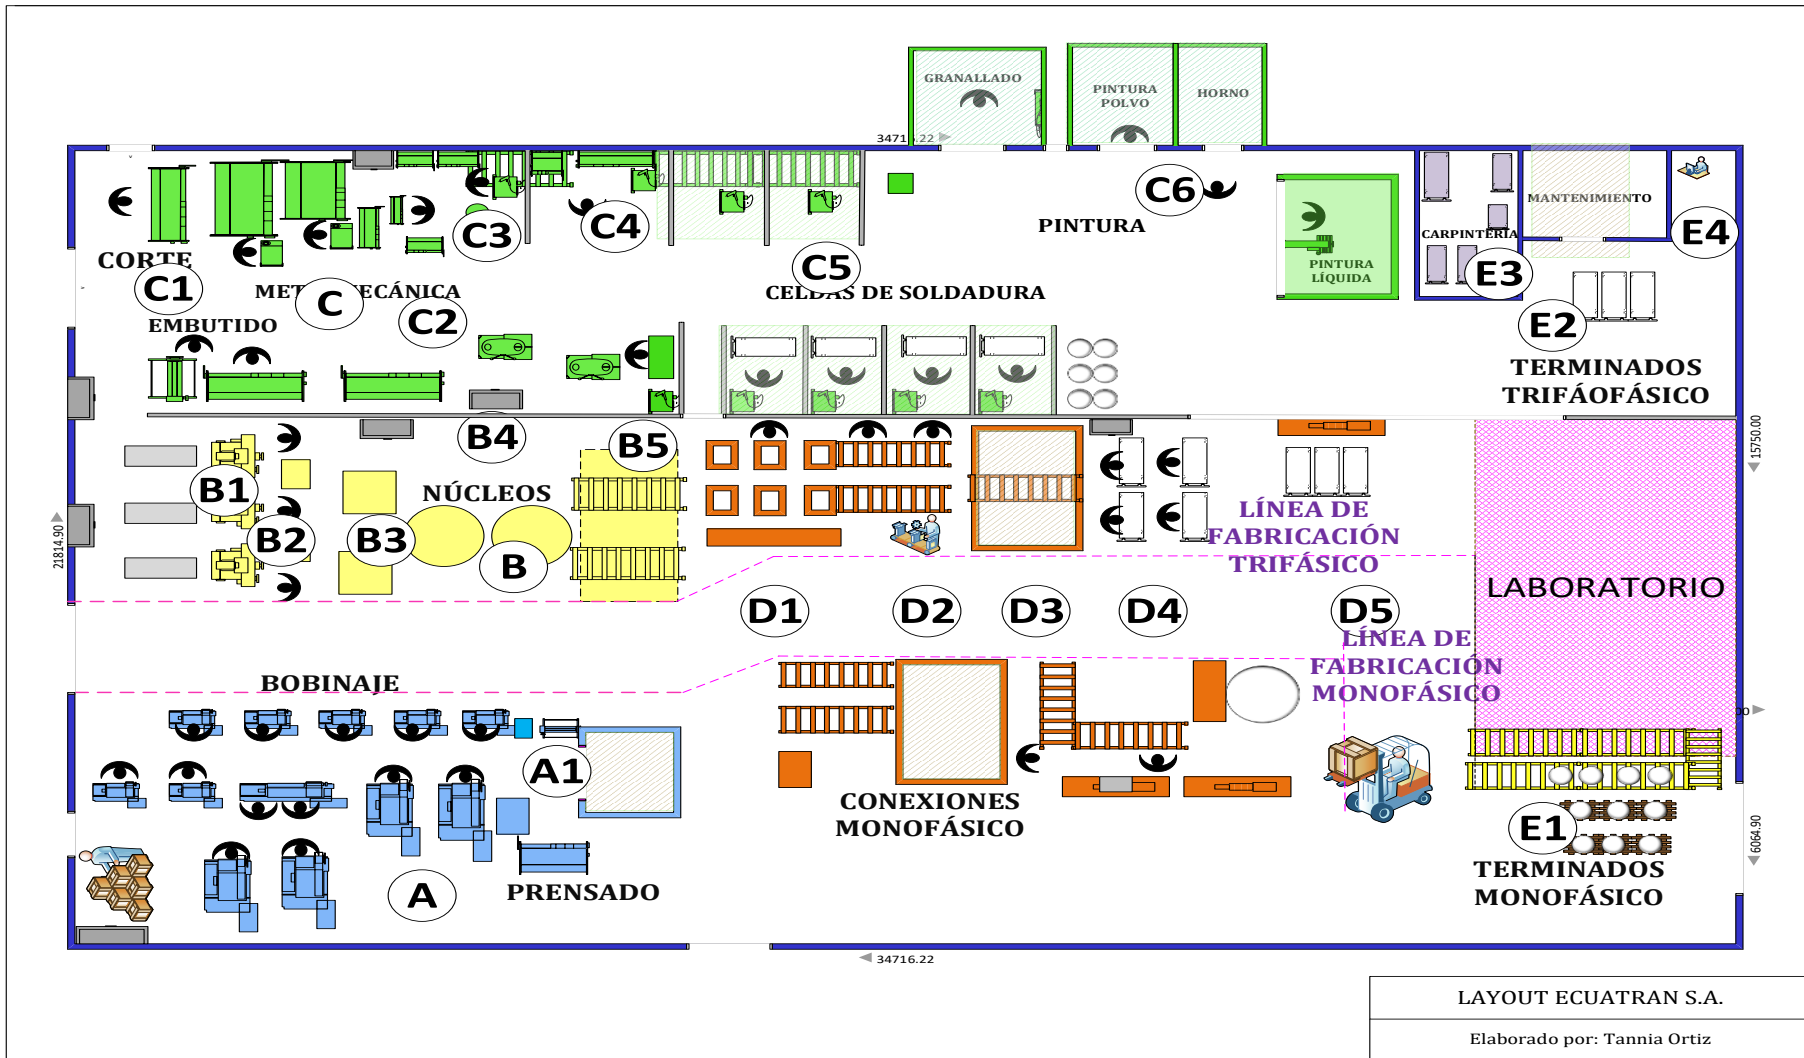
Layout de la planta de producción Ecuatran S.A. [18].
